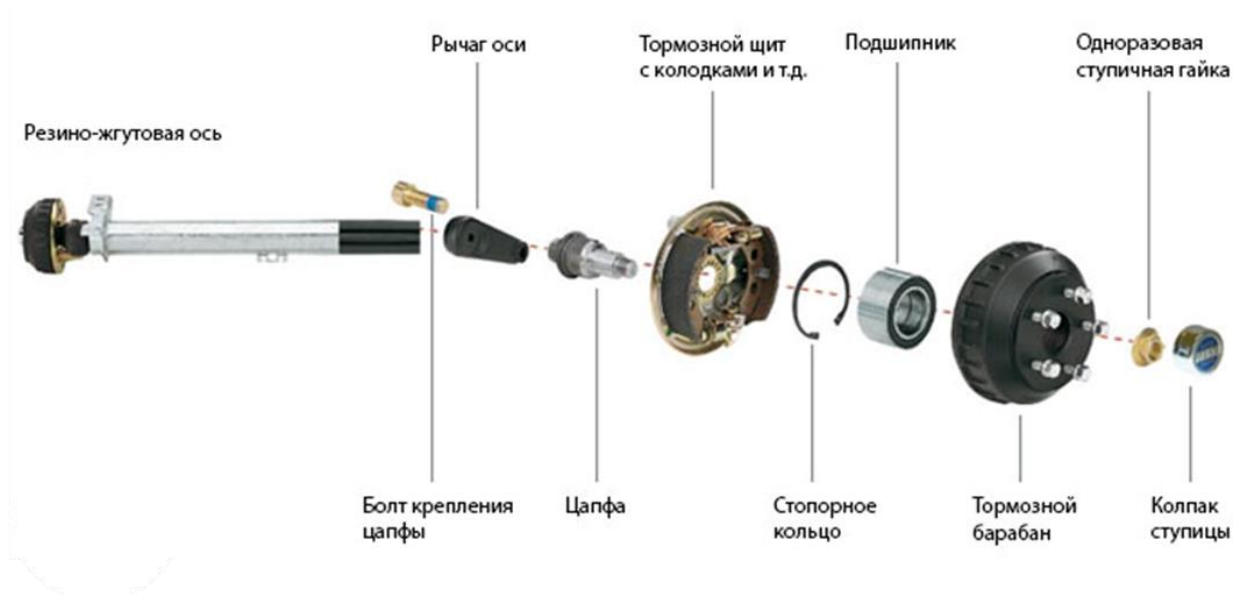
Крепление тормозного щита и барабана к резино-жгутовой оси
